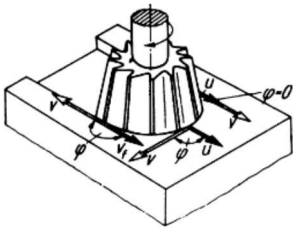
Vorschubrichtungswinkel φ beim Fräsen mit Stirnfräser (nach DIN 6580)
